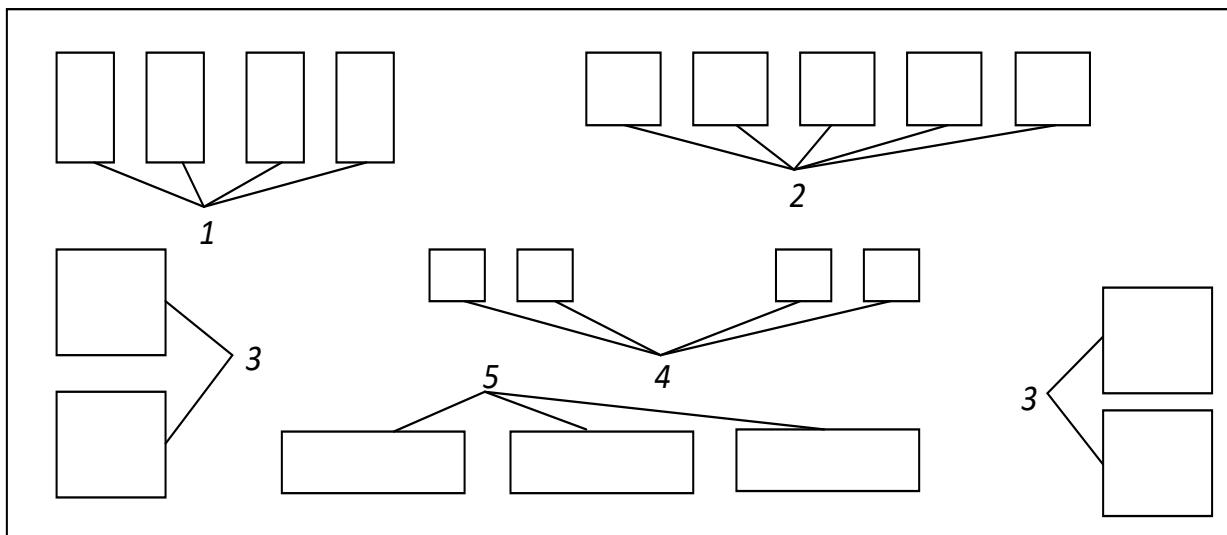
План расстановки оборудования механосборочного цеха: 1, 2 – металлорежущие станки; 3 – универсальный станок; 4 – сверлильный станок; 5 – фрезерный станок
